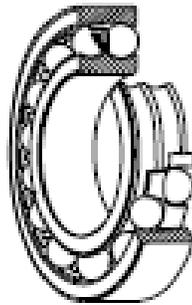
Rodamientos de bolas autoalineantes
